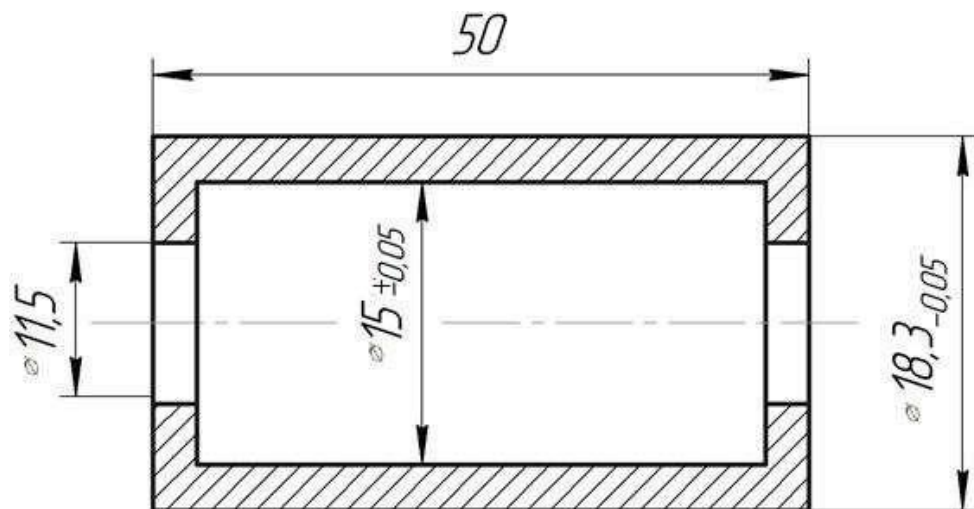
Сталева втулка для пружинного конічного вкладиша
